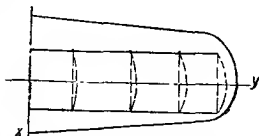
Элементы металлического крыла. Сплошные линии показывают основную конструкцию.
